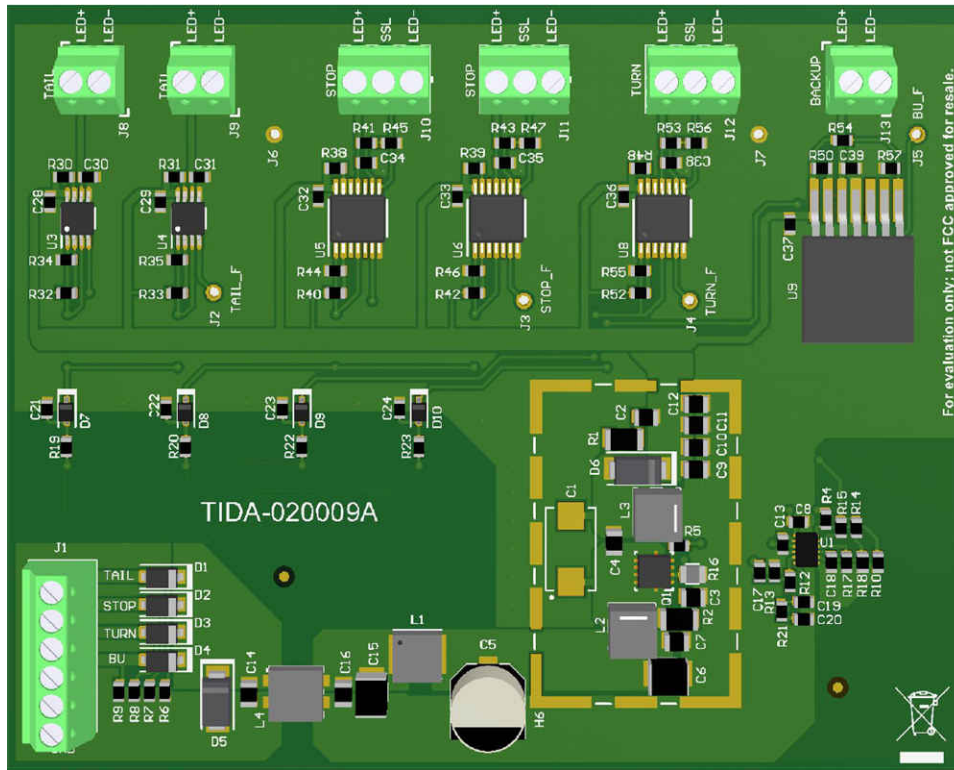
TIDA-020009 PCB의 3D 렌더링
